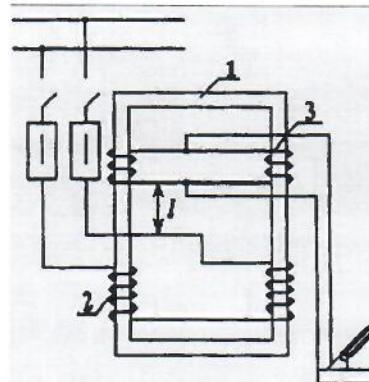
Конструктивная схема сварочного трансформатора
